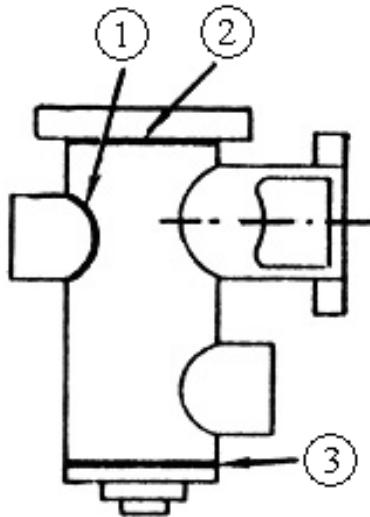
Дефекты грязевика котла, ремонтируемые сваркой
